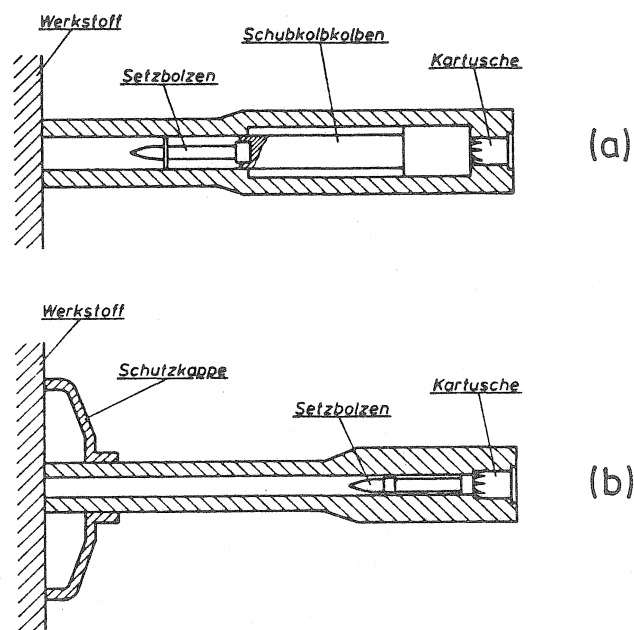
Prinzipskizze zum konstruktiven Aufbau von Bolzensetzwerkzeugen
